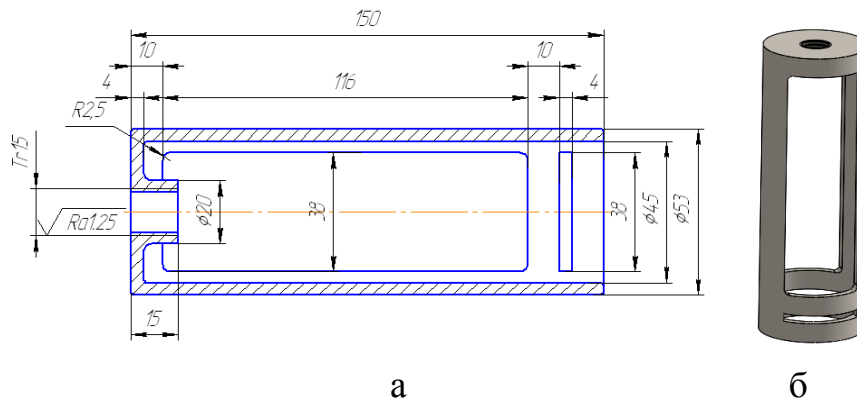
Креслення (а) й 3D-модель корпусу
